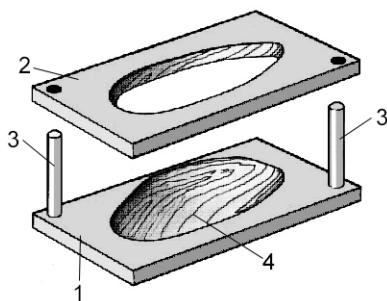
Конструкція найпростішого пресу для формування деталей з листової термопластичної пластмаси:
